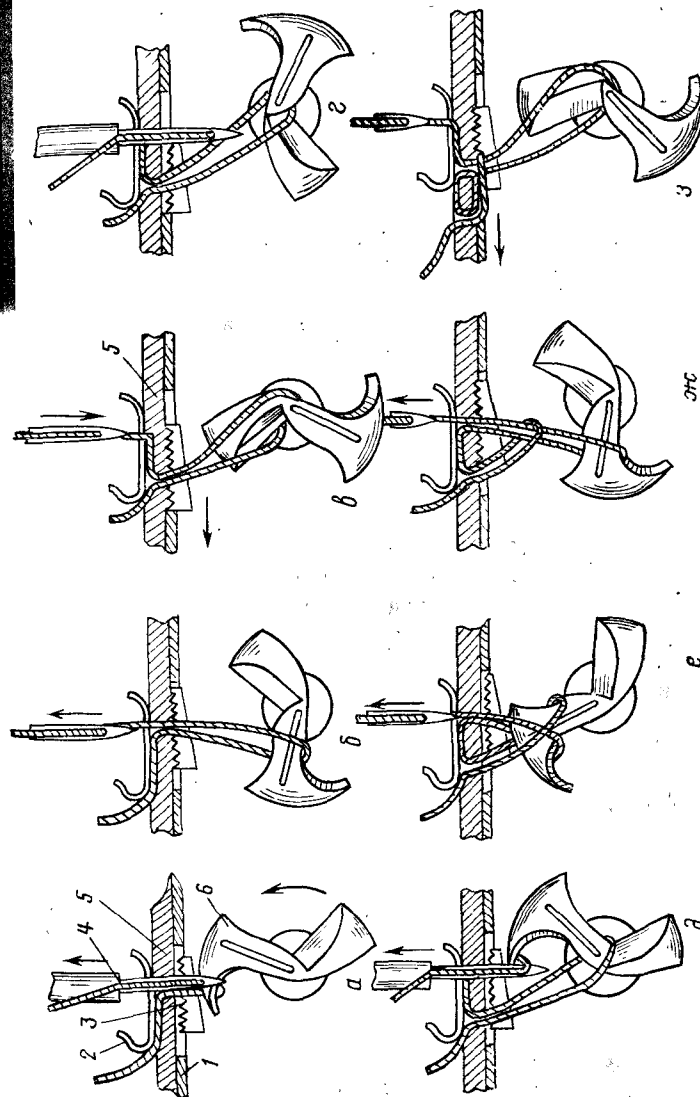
Процесс образования однониточного цепного стежка вращающимся петлителем: 1 — игольная лапка; 2 — прижимная лапка; 3 — игла; 4 — режка; 5 — материал; 6 — петлитель
